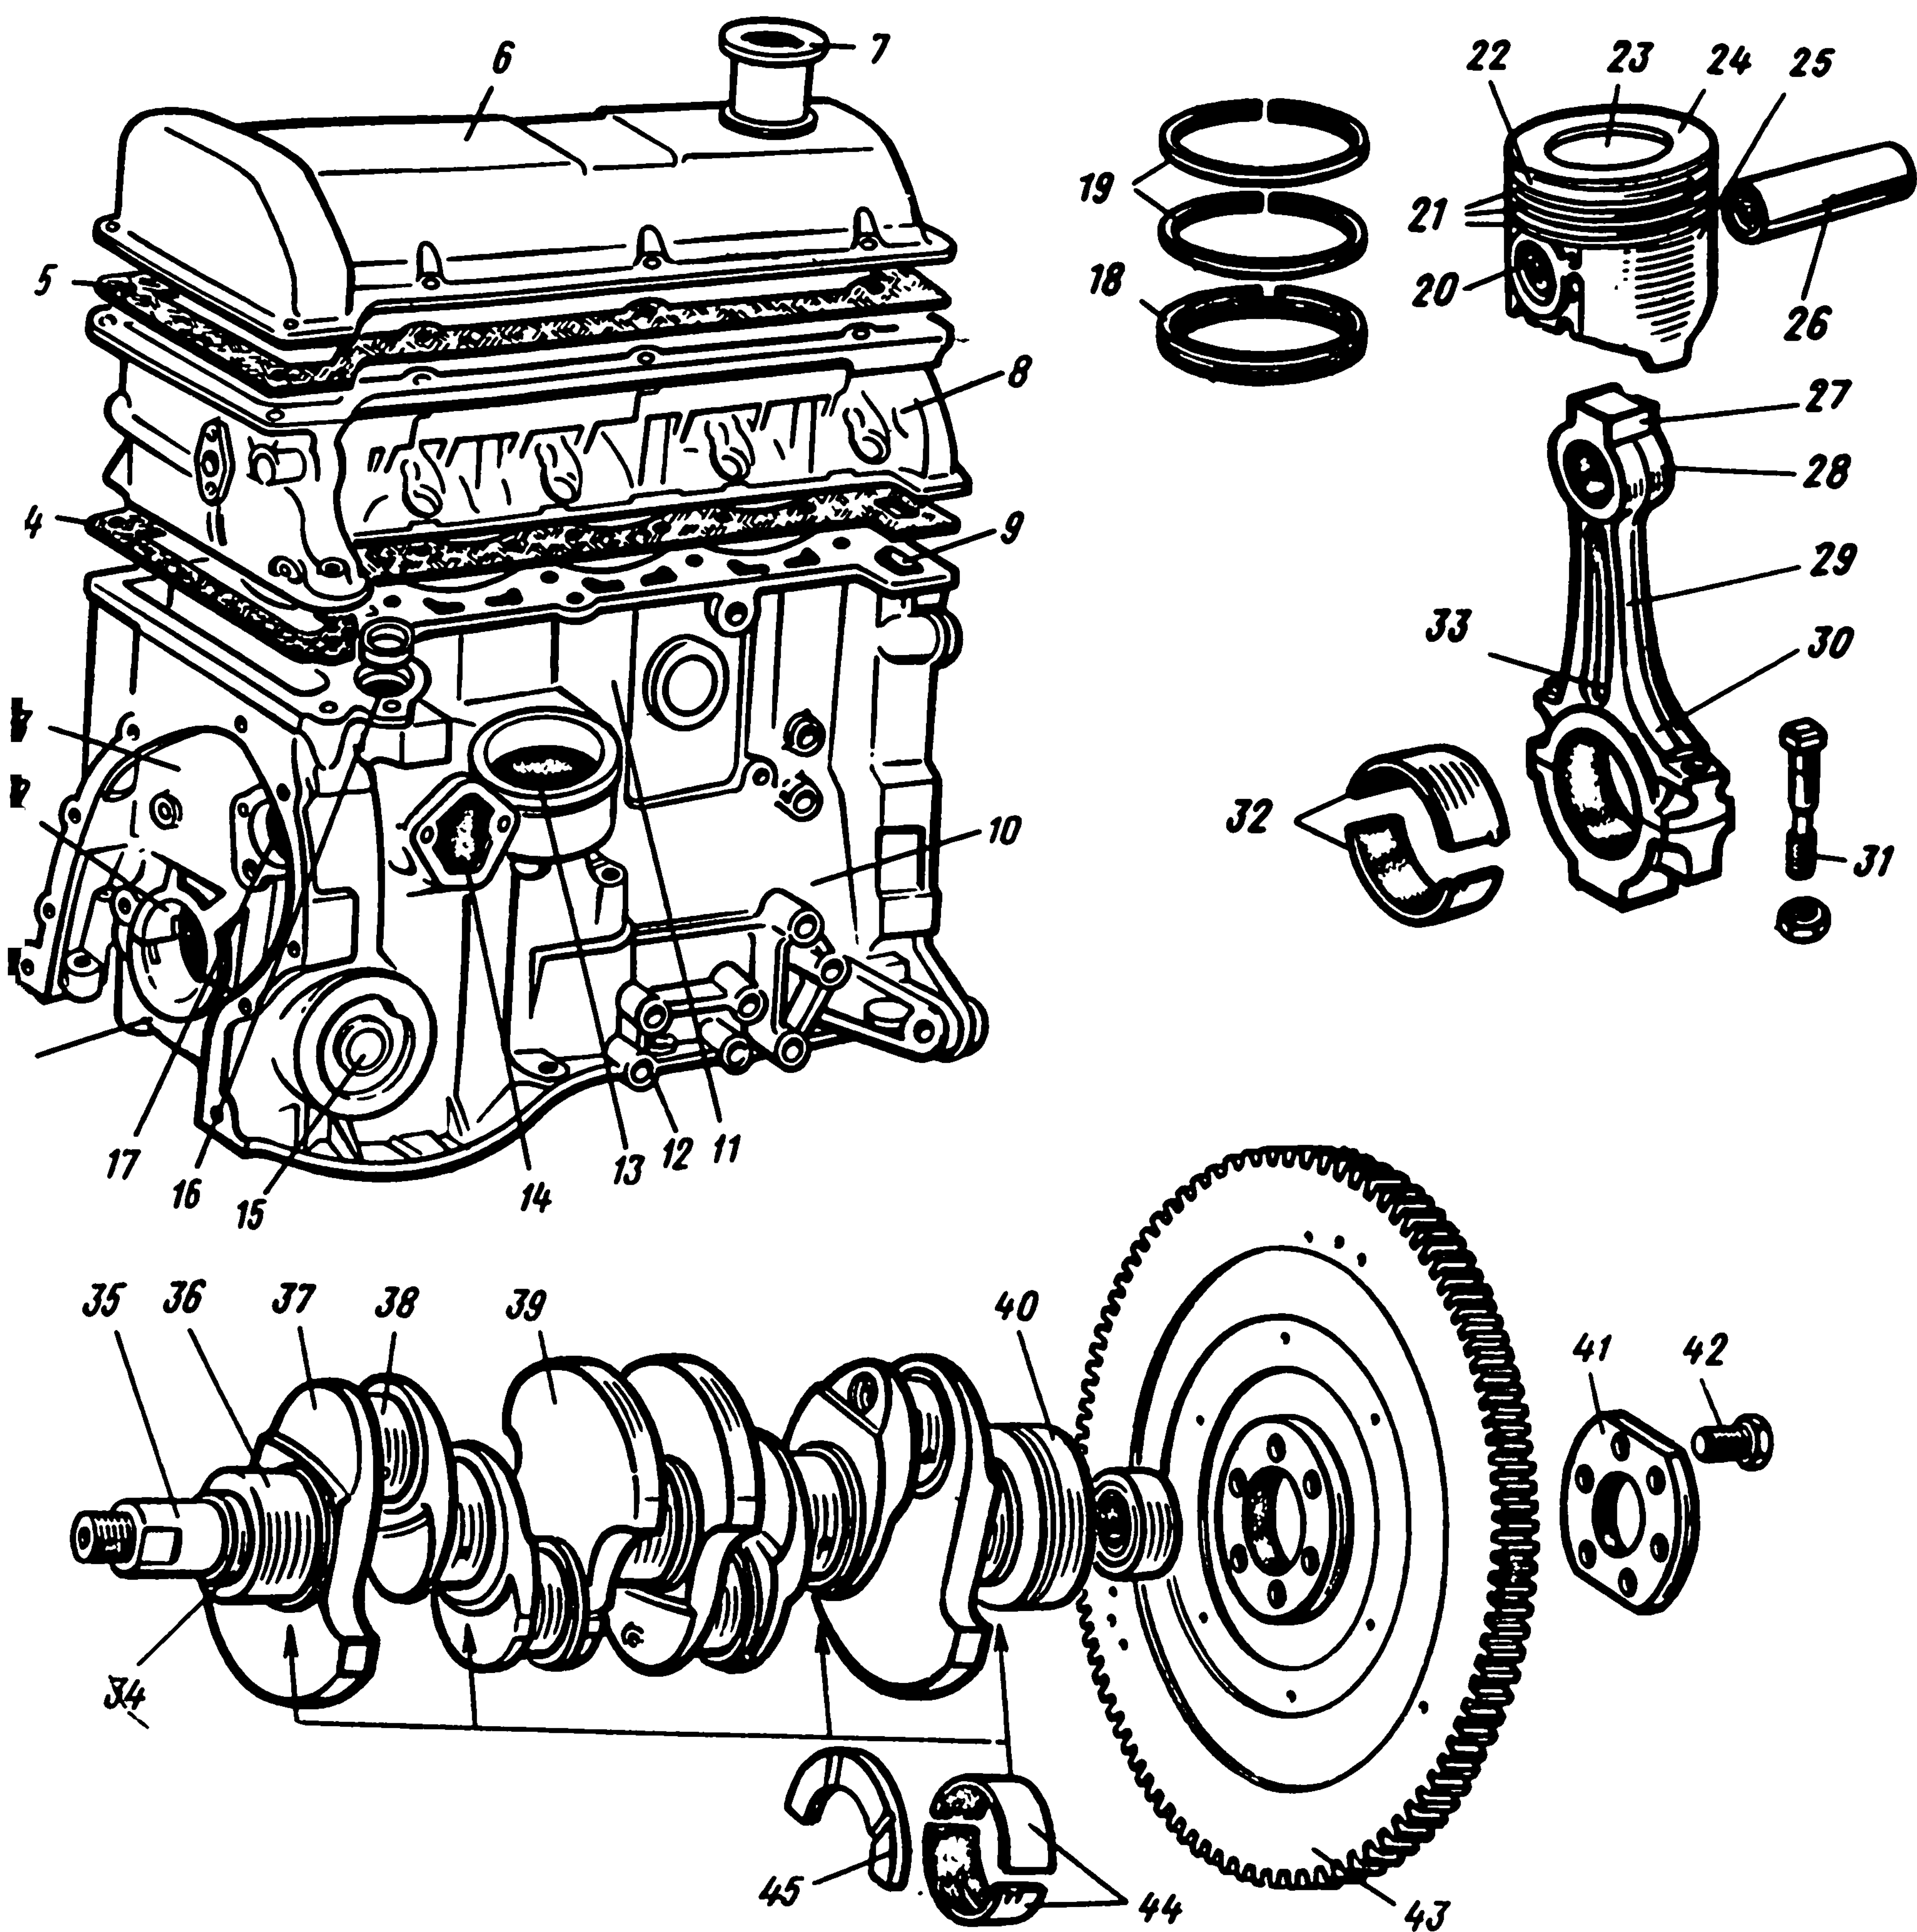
Кривошипно-шатунный механизм двигателя VA3-2121
